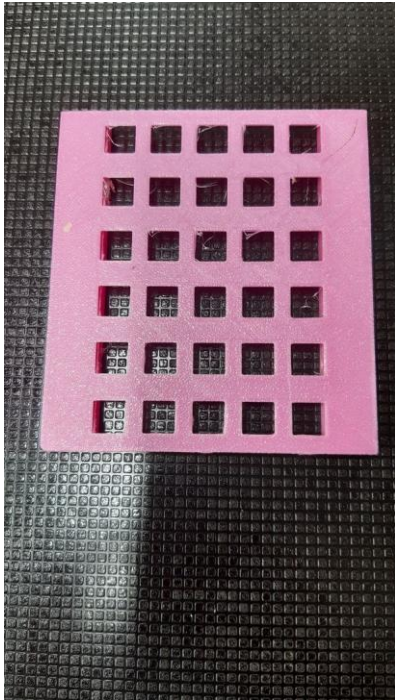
Erster 3D Druck Wagen Ansicht oben
